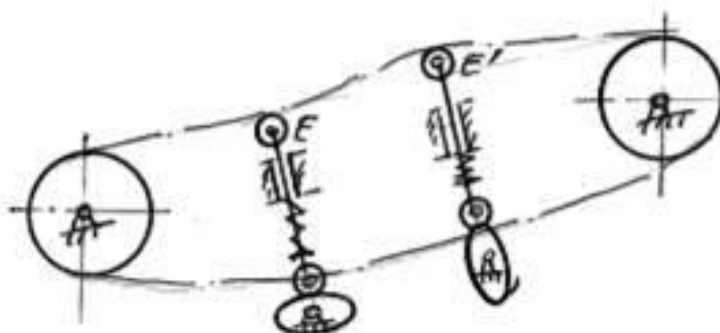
Сдвоенный кулачковый механизм встряхивателя
